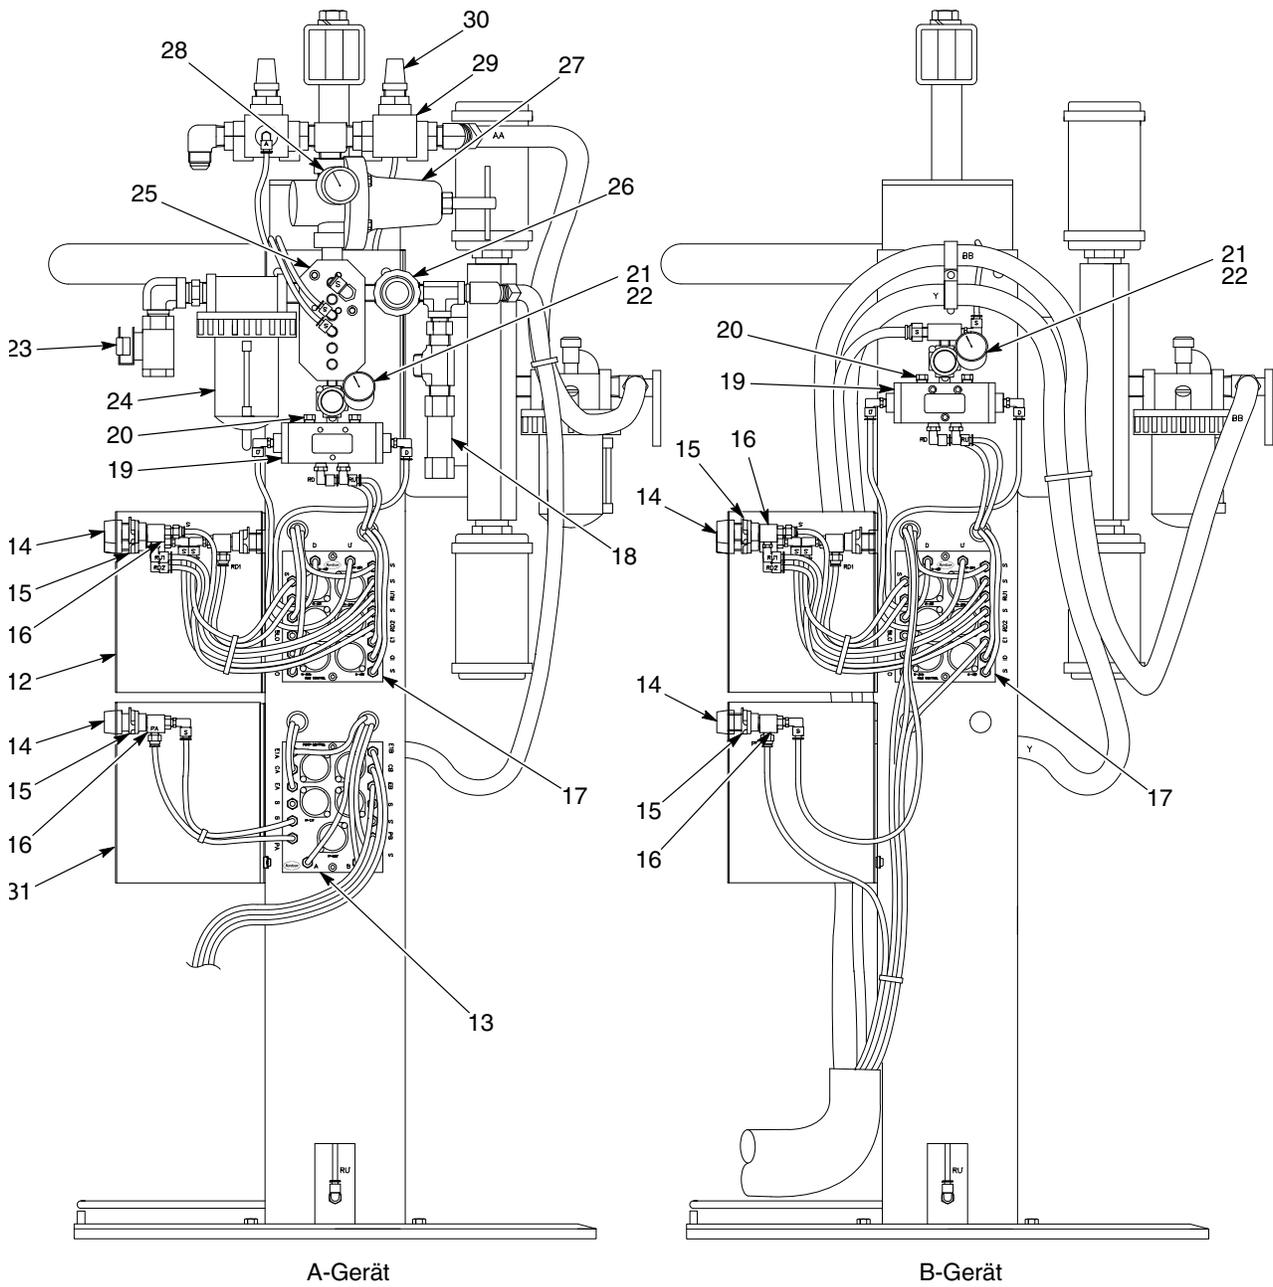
Pneumatische Komponenten des Fassentleerers mit Hubwerk-Zweihandschalter, Frontalansicht
